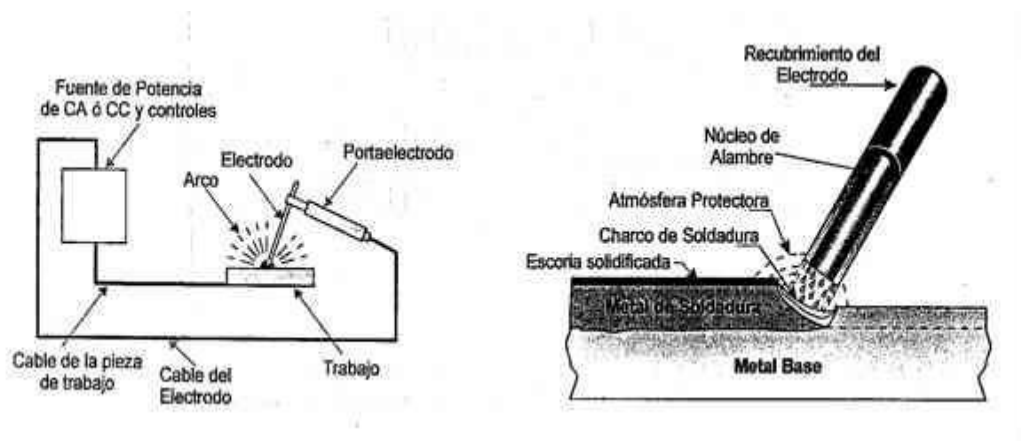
La soldadura de arco metálico con electrodo revestido
